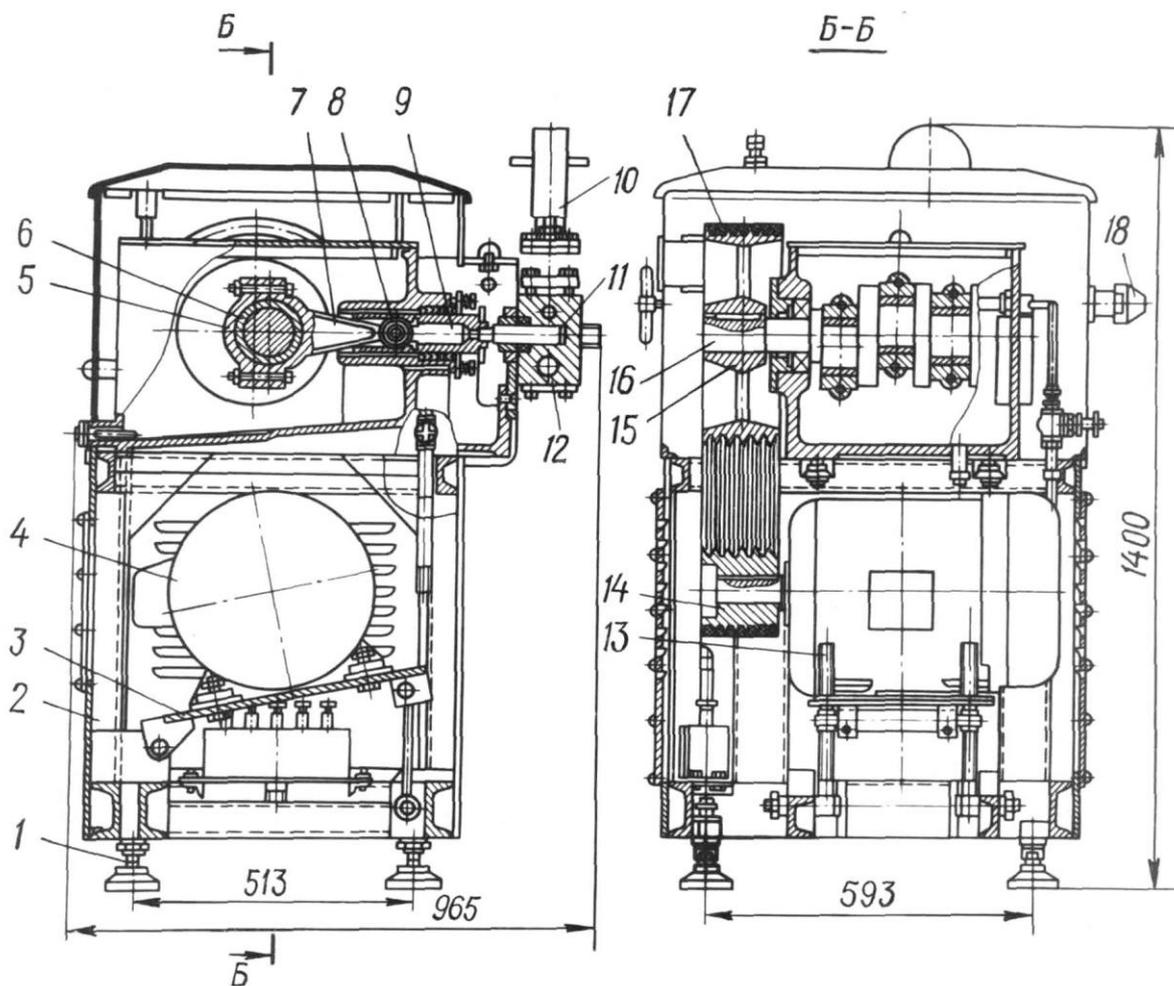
Общий вид гомогенизатора марки К5-ОГА-1,2: 1 – опора; 2 – станина; 3 – плита; 4 – электродвигатель; 5 – кривошипно-шатунный механизм; 6 – вкладыш; 7 – шатун; 8 – палец; 9 – ползун; 10 – манометрическая головка; 11 – плунжер; 12 – плунжерный блок; 13 – устройство для натяжения ремней; 14 – ведущий шкив; 15 – ведомый шкив; 16 – коленчатый вал; 17 – клиновой ремень; 18 – предохранительный клапан
